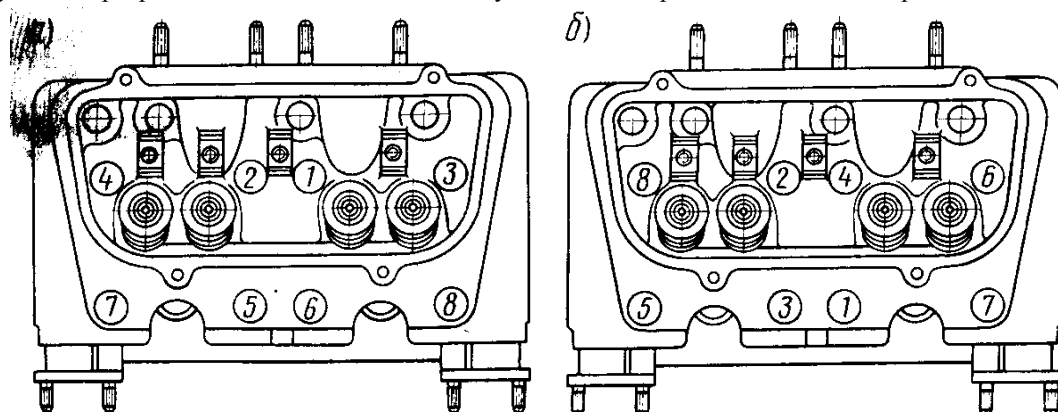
Порядок затяжки гаек головок цилиндров: а—предварительный момент затяжки 1,6...2 кгс- м; б—окончательный момент затяжки 4...5 кгс- м
